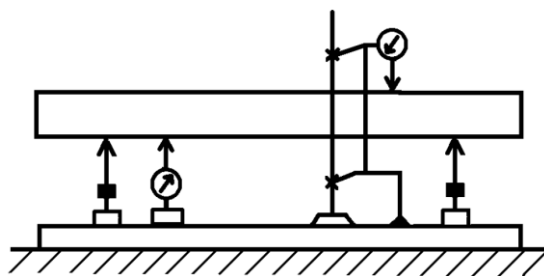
Příklad požadavku geometrické tolerance a jeho popis.
